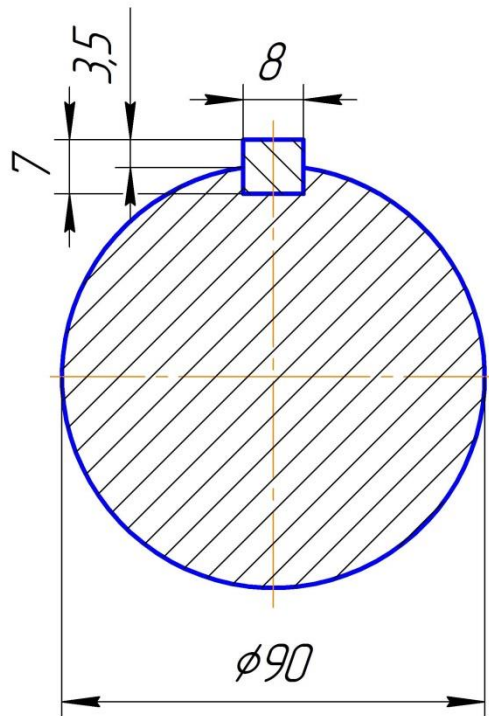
Ескіз шпонкового з'єднання вала з робочим колесом
